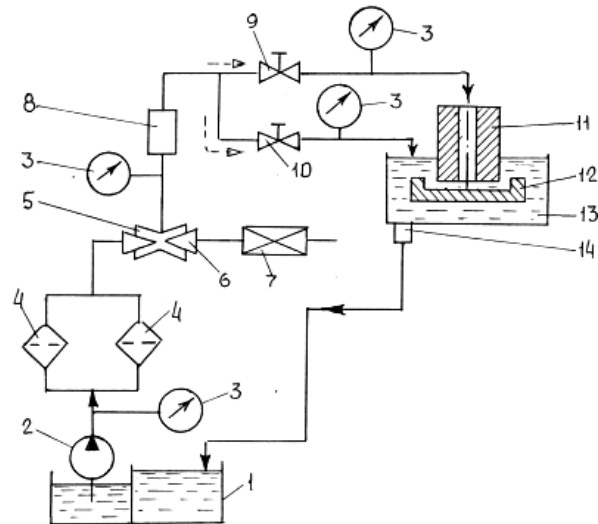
Схема гідравлічної системи верстату: 1 – бак; 2 – помпа; 3 – манометри; 4 – фільтр; 5 – пристрій для регулювання витрачання робочої рідини; 6 – заслонка; 7 – перетворювач; 8 – ротаметр; 9, 10 – крани; 11 – порожнистий електрод-інструмент; 12 – заготовка; 13 – робоча ванна; 14 – зливний отвір
